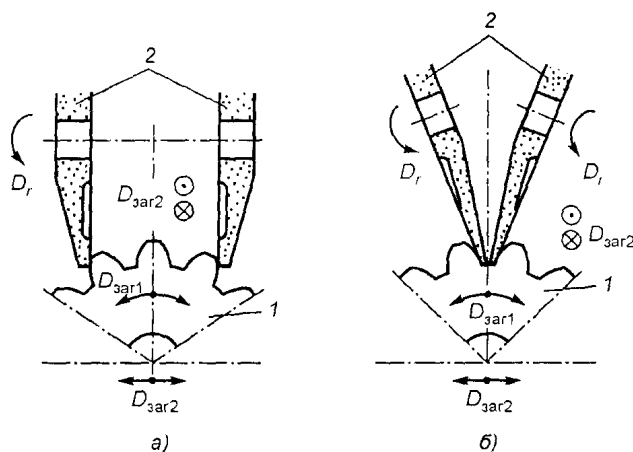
Схемы шлифования зубьев тарельчатыми шлифовальными кругами
